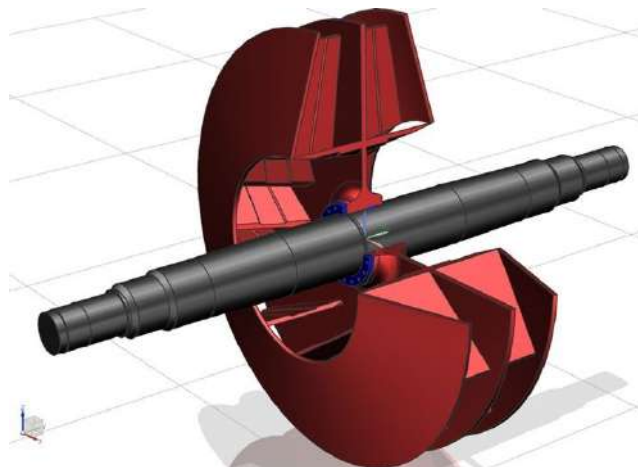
Конструктивная схема соединения вала с колесом крыльчатки вентилятора
